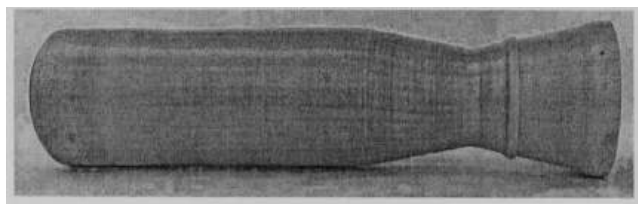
Внешний вид корпуса изделия "Вампир" из стеклопластика [1]
